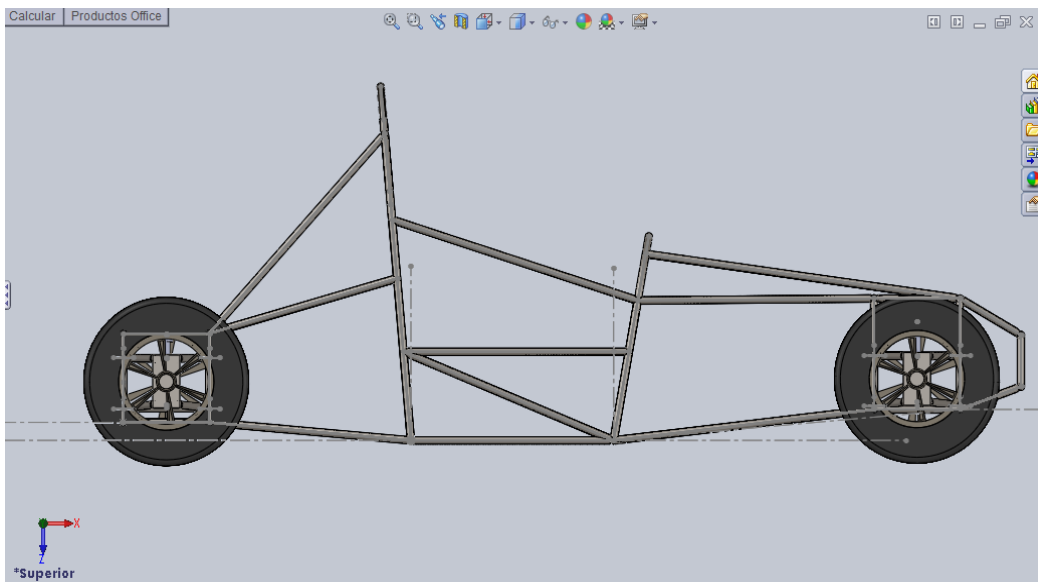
Vista lateral del ensamblaje Pull-rod
